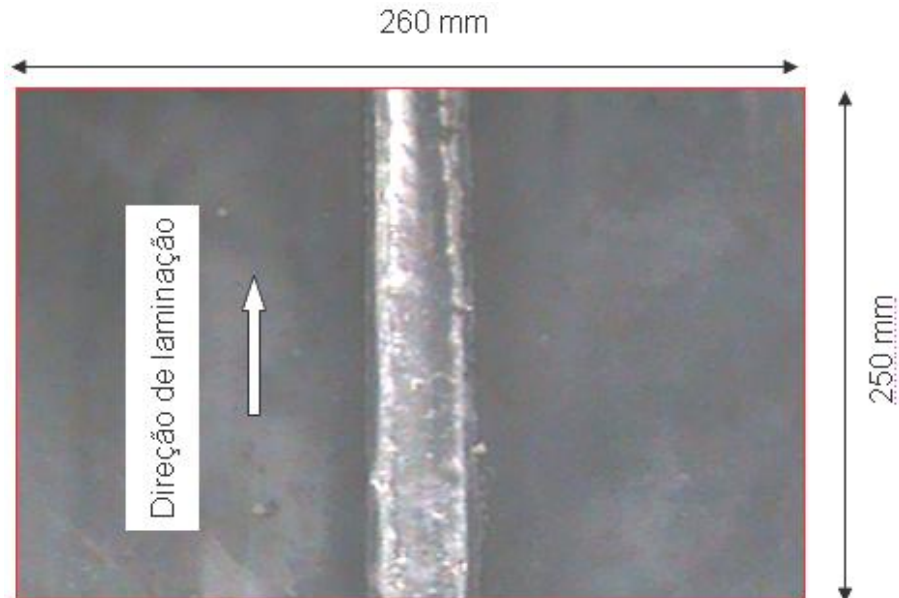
Fotografia das chapas soldadas mostrando a orientação da direção de laminação e do cordão de solda.
